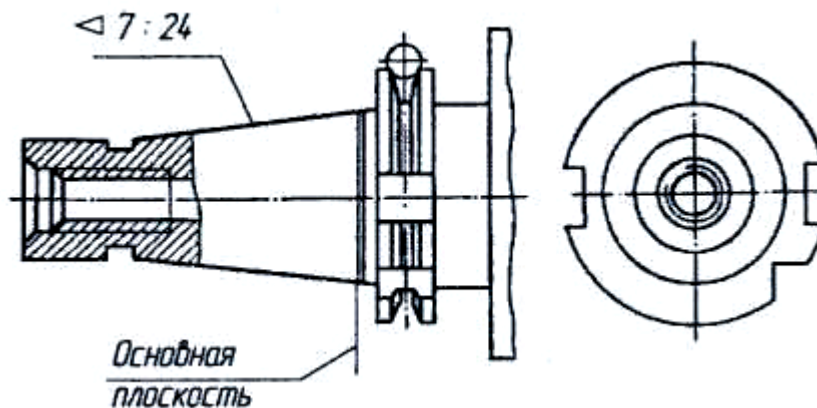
Хвостовик шпиндельных оправок станков сверлильно-фрезерно-расточной группы
